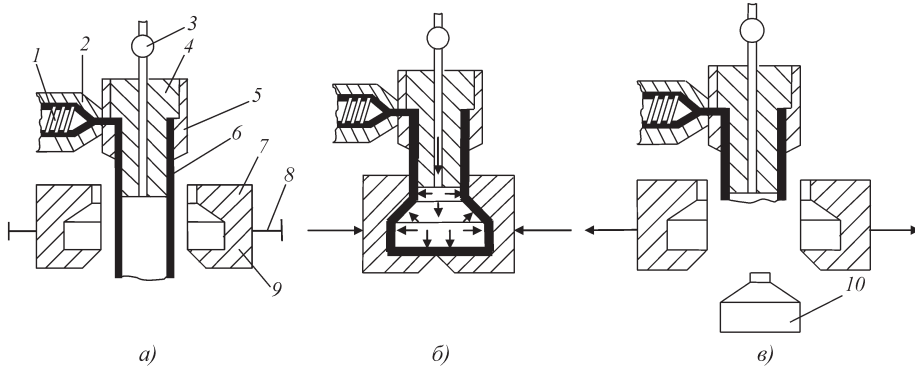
Технологическая схема процессов экструзии трубчатой заготовки (а), ее раздув и формование изделия (б) и съем (в) изделия (каналы в форме для выхода вытесняемого раздуваемой заготовки воздуха не показаны):
